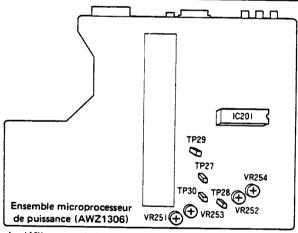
Réglage de la vitesse de défilement de la bande
